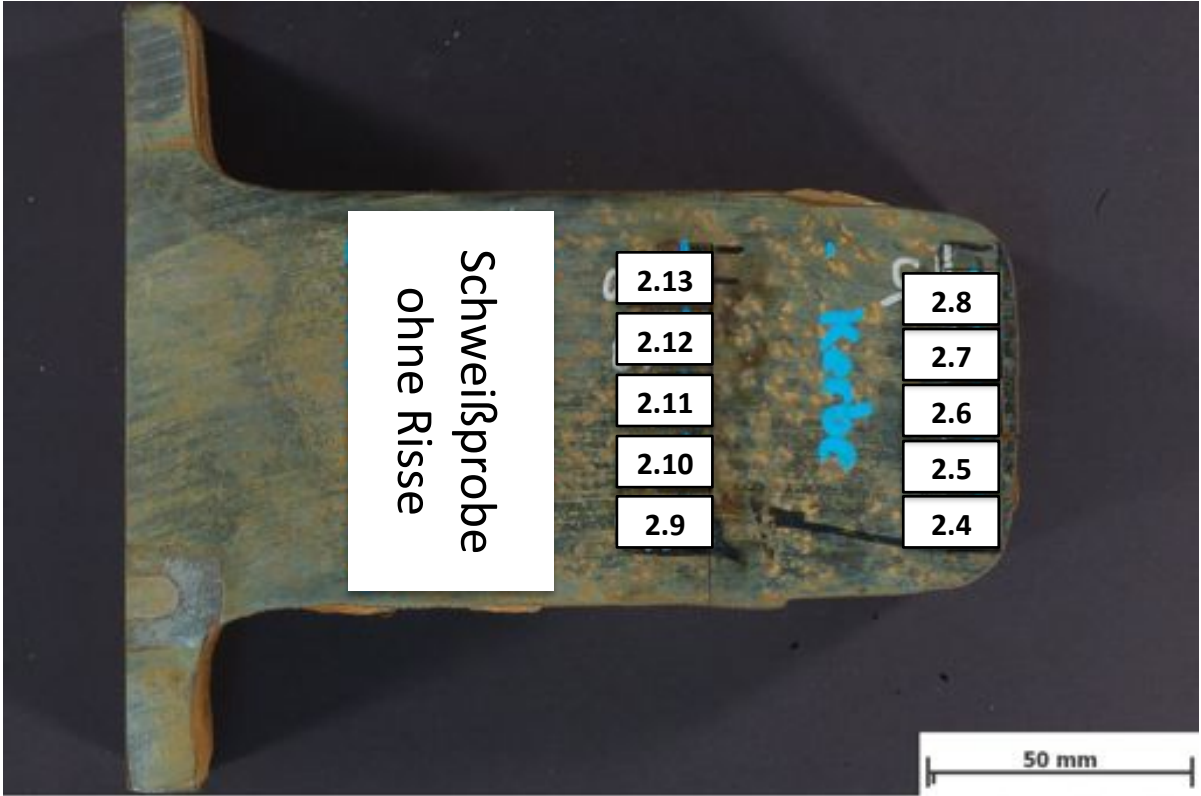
Übersicht Kerbschlagbiegeprobenentnahme der Proben 2.4-2.13; Schweißprobe ohne Risse
